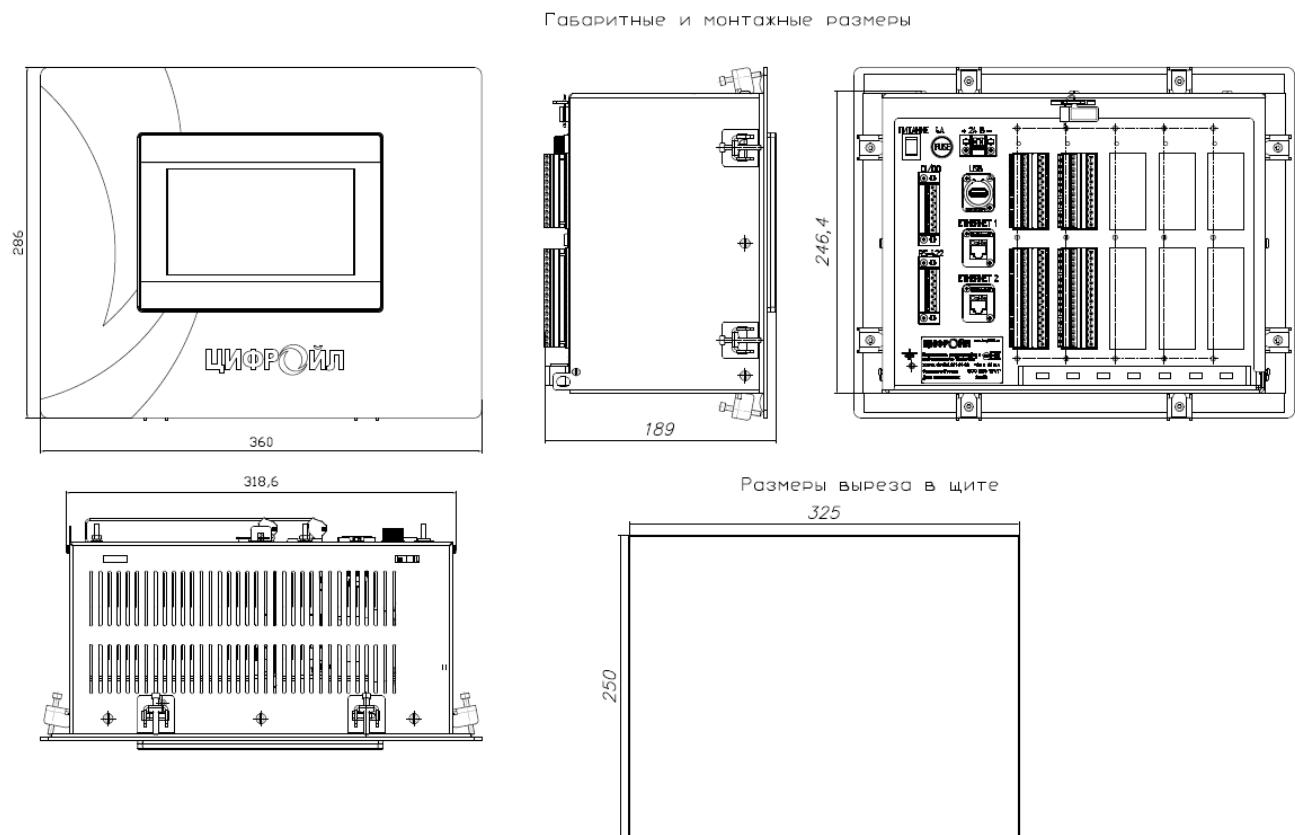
Габаритные размеры вычислителя расхода для крепления в шкаф
